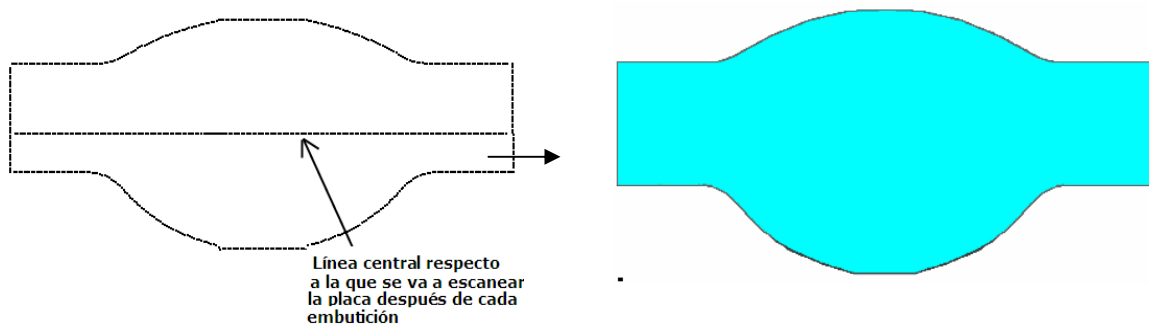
Placa creada a partir del escaneado inicial de la real
